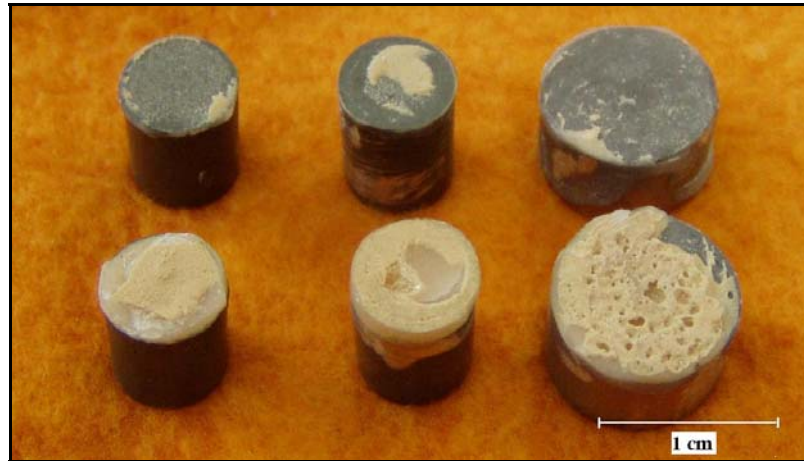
Detalhe das superfícies de fratura dos corpos-de-prova cilíndricos.
